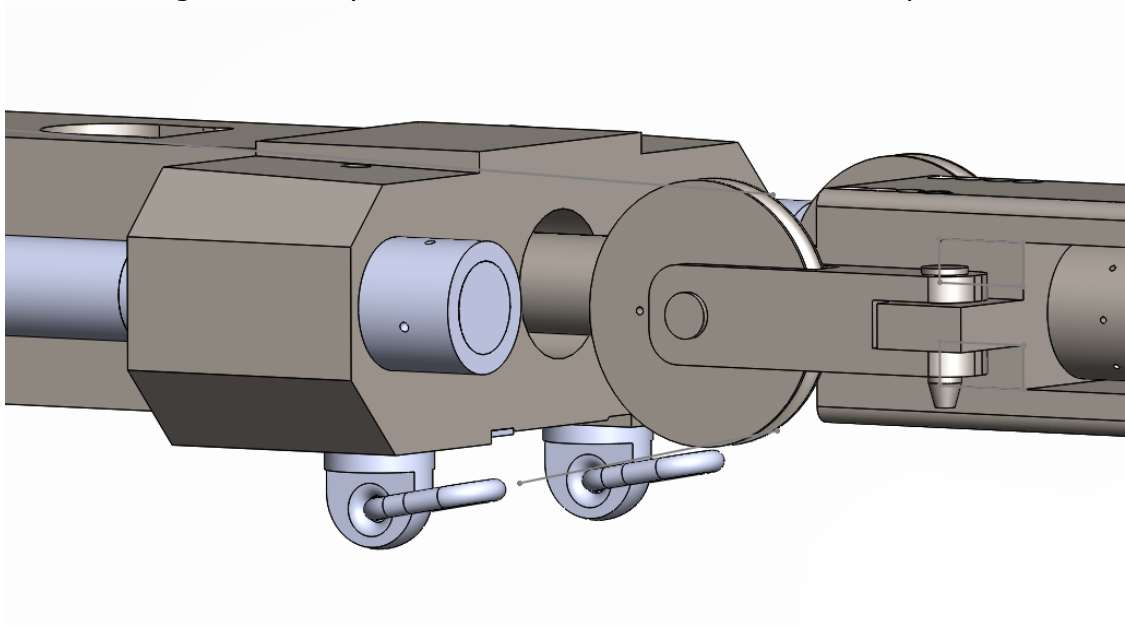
Image 3d de la possible installation des treuils sur la pièce 8204-1
